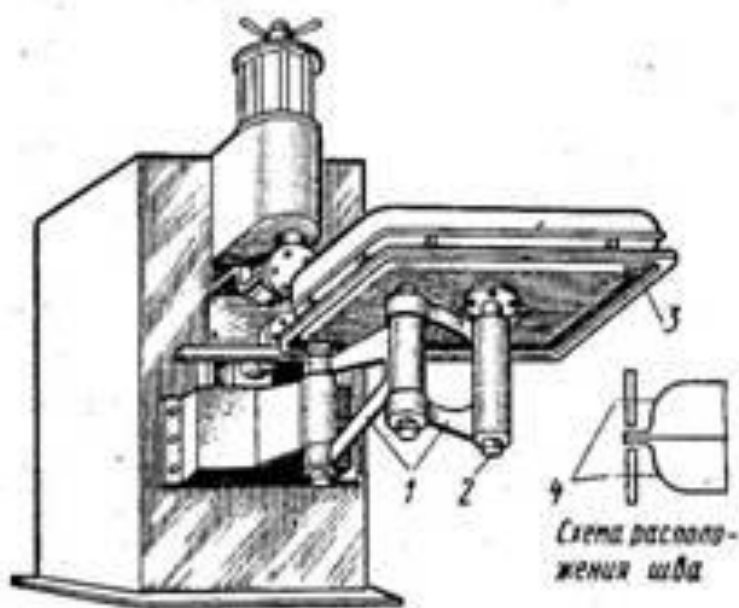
Сварка на универсальных контактных машинах с использованием механизированных и автоматизированных приспособлений
